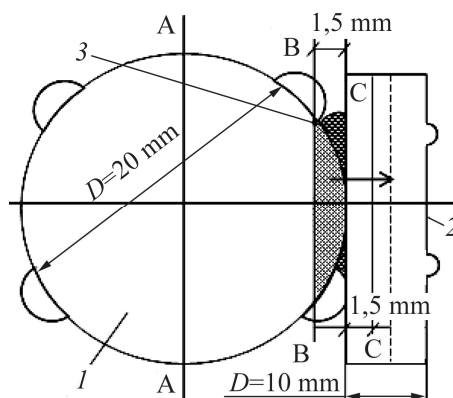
Схема вимірювання мікротвердості в термозміцненій арматурі і зварному з'єднанні: 1 – основна; 2 – поперечна; 3 – зварний шов.
